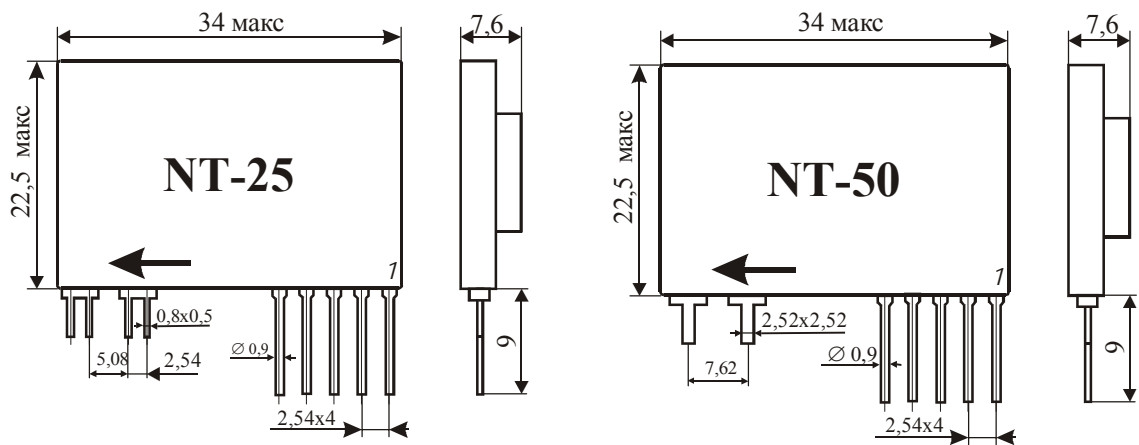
Внешний вид и габаритные размеры датчиков тока типа NT-25 и NT-50
